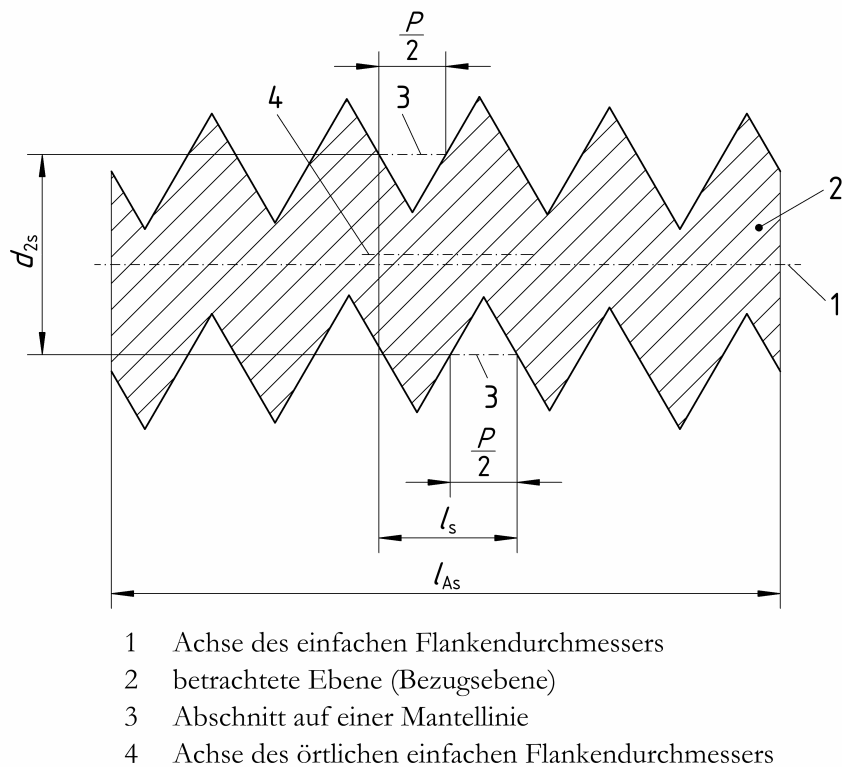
einfacher Flankendurchmesser eines zylindrischen eingängigen Außengewindes
